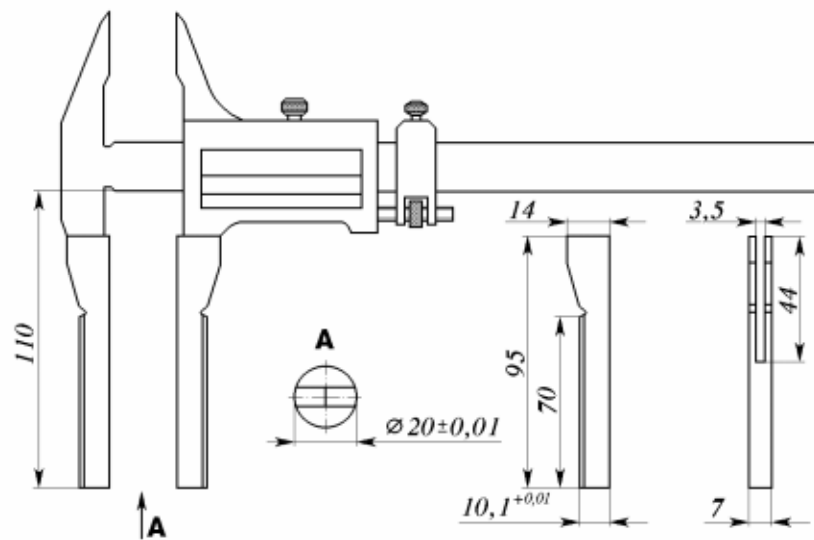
Штангенциркуль для замера натяга манжеты цилиндра подвески
